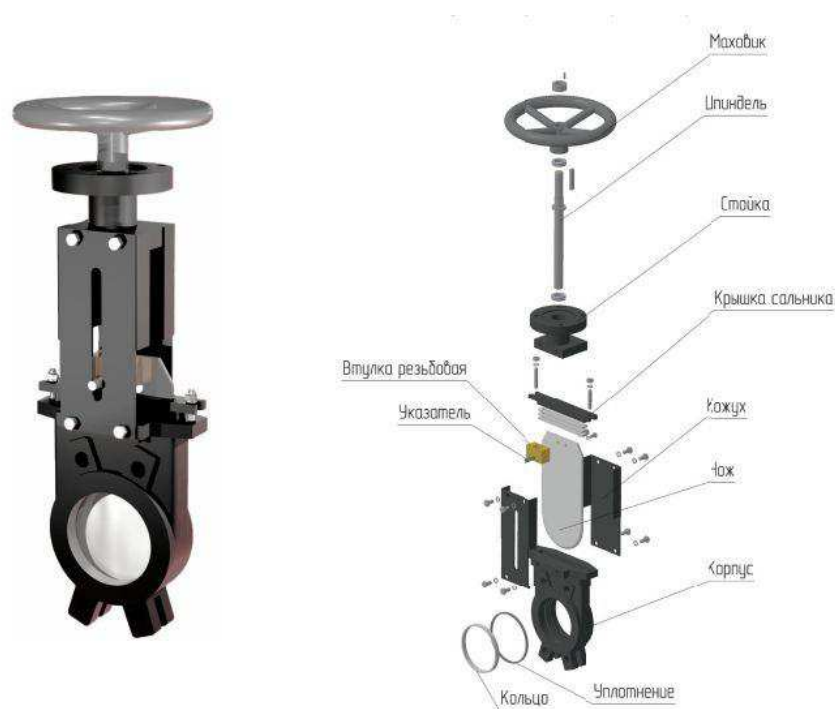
Вид и конструкция шиберной задвижки
